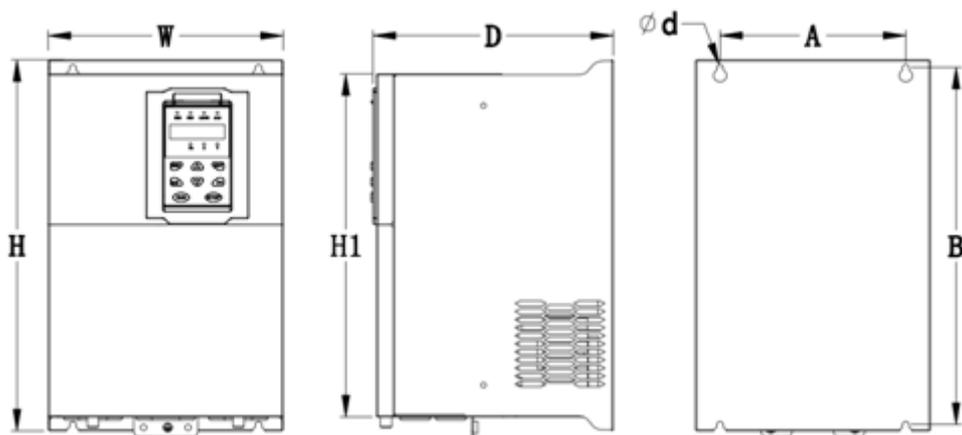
TAMAÑO D ~ G (18.5KW-90KW) Dimensión
